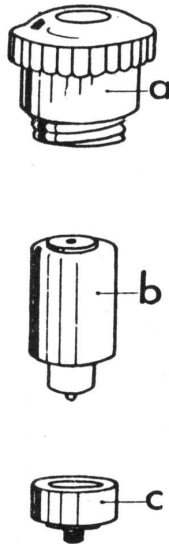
Cortacircuito fusible Diazed de la forma Siemens. a) Tapón roscado. b) Cartucho fusible. c) Tornillo de ajuste
